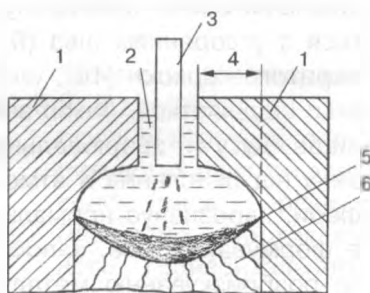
Схема електрошлакового зварювання: 1 - зварюваний метал, 2 - шлакова ванна, 3 - електродний дріт, 4 - величина проплавлення кромок металу, 5 - металева ванна, 6 - зварювальний шов
